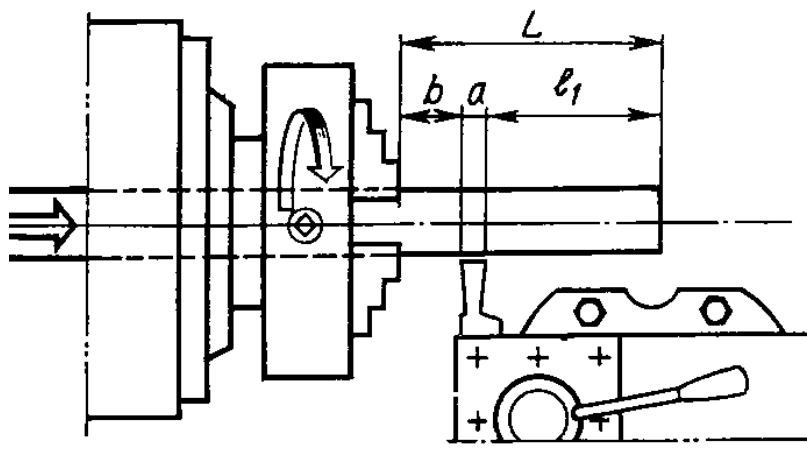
Схема к определению вылета заготовки из патрона при отрезке детали
